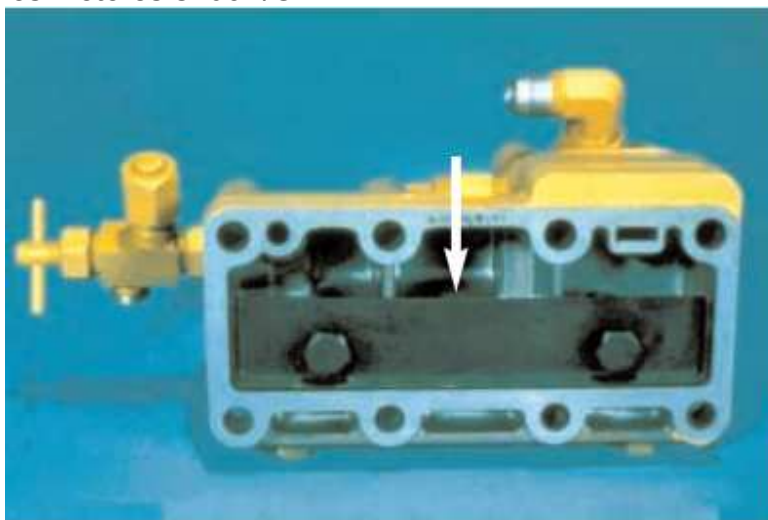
Tapa del múltiple de combustible del Motor 3306
